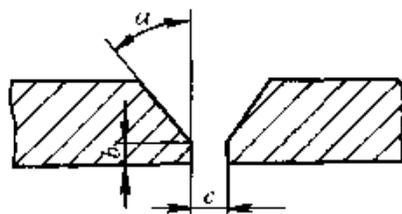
“单面焊双面成形”的接头组对尺寸
